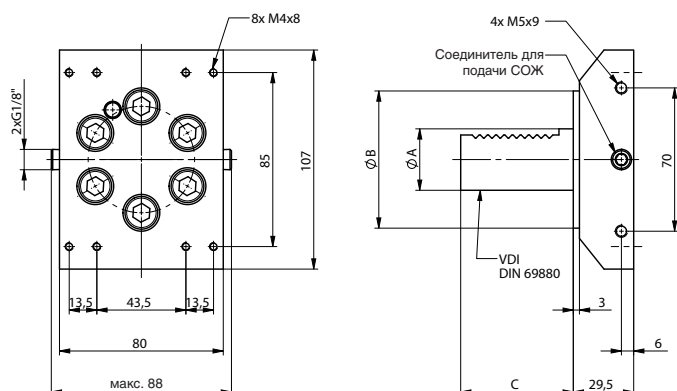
Станочный адаптер с прямым хвостовиком для дисковой револьверной головки с держателем инструмента VDI, тип 9119AB...S
